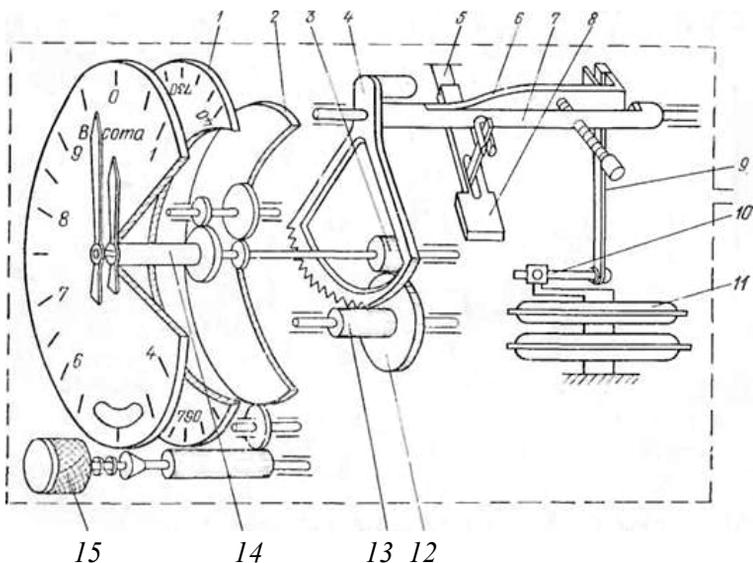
Кинематическая схема двухстрелочного высотомера:
